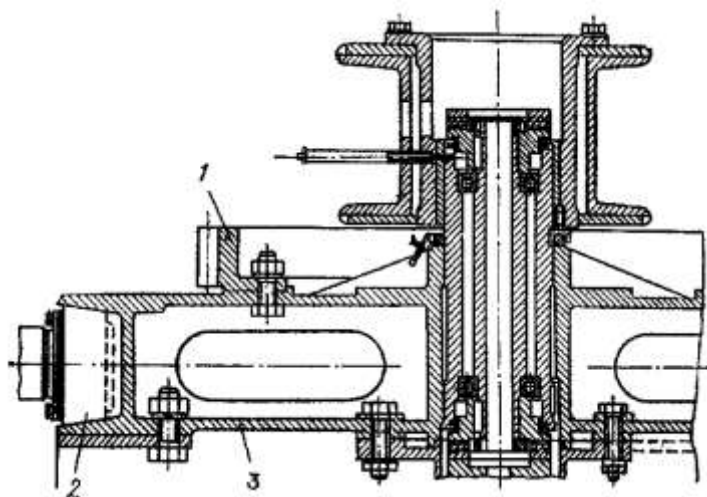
Схема опорно-поворотного устройства автомобильного крана
